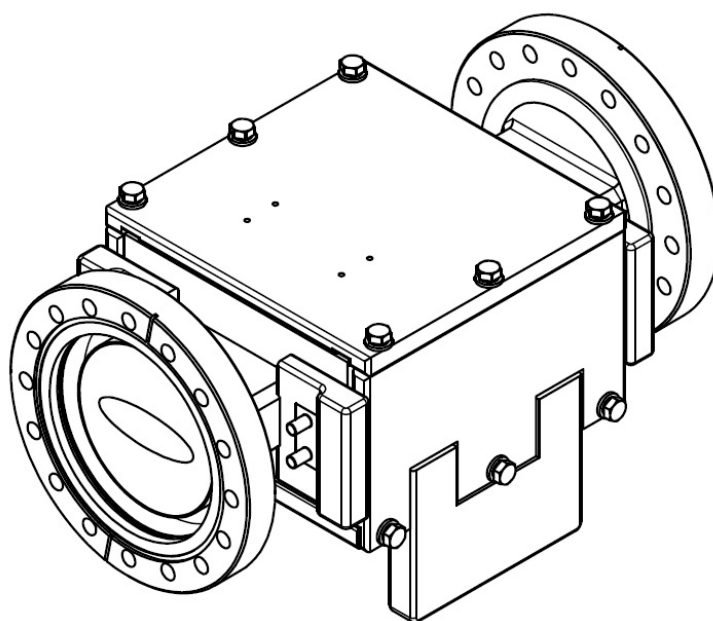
Сборка кикера с вакуумной камерой
